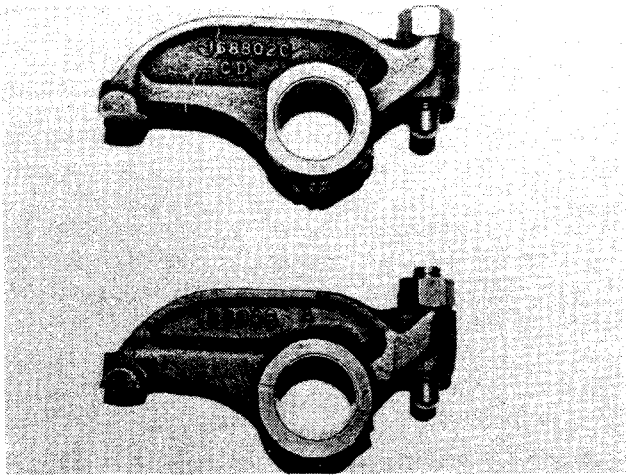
, (V40305). Indicación de grietas por inspección magnética.
